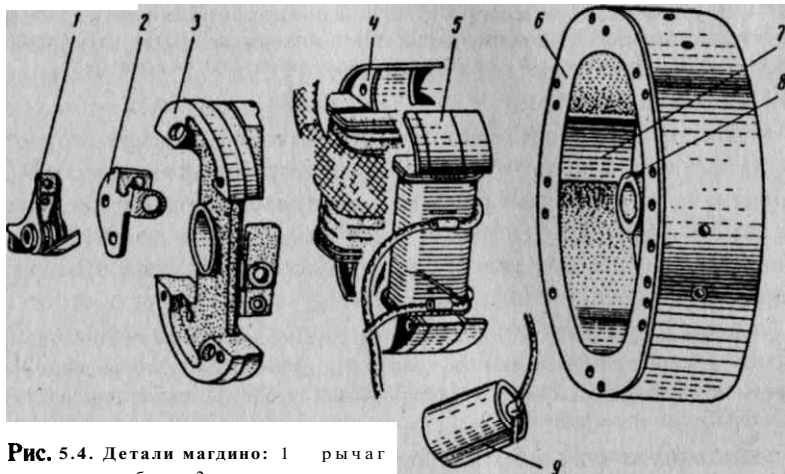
Детали магдино: 1 — рычаг прерывателя в сборе; 2 — держатель контакта в сборе; 3 — основная пластинка; 4 — катушка зажигания; 5 — катушка освещения; 6 — ротор в сборе; 7 — постоянный магнит; 8 — втулка; 9 — конденсатор
